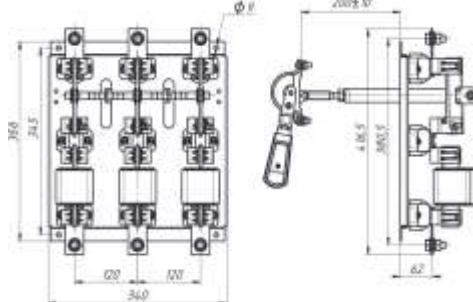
Разъединитель-предохранитель серии РПС-6
